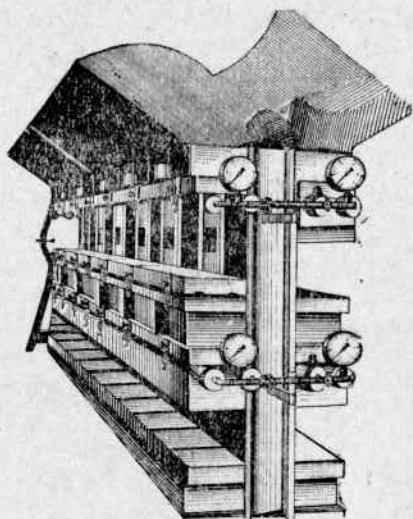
Схема одновременной запрессовки в одной секции прессы двух заготовок для полок большого сечения.
